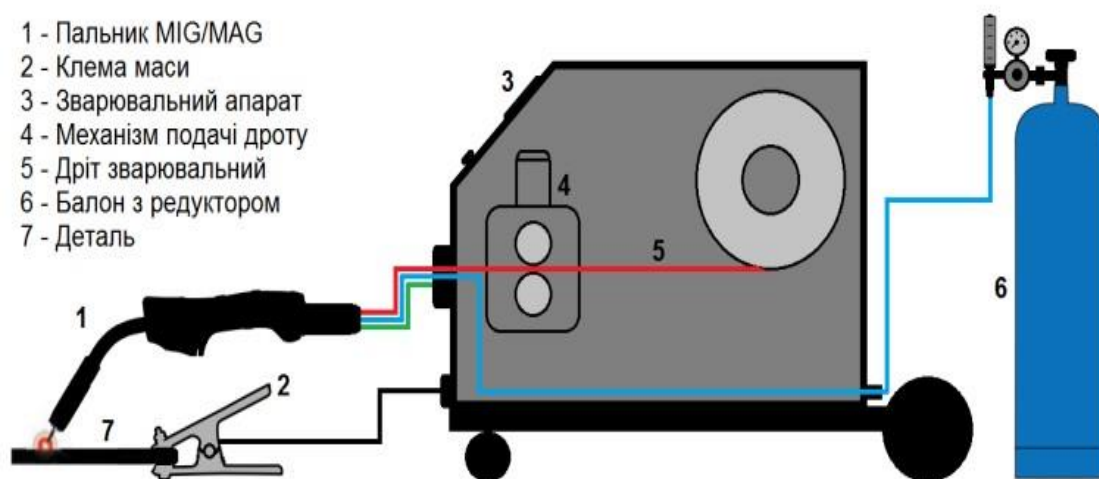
Схема процесу напівавтоматичного зварювання CO₂[8].
